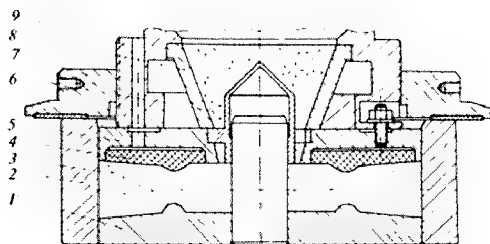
Схема дозирования и укладки формовочной смеси в пресс-форму:
